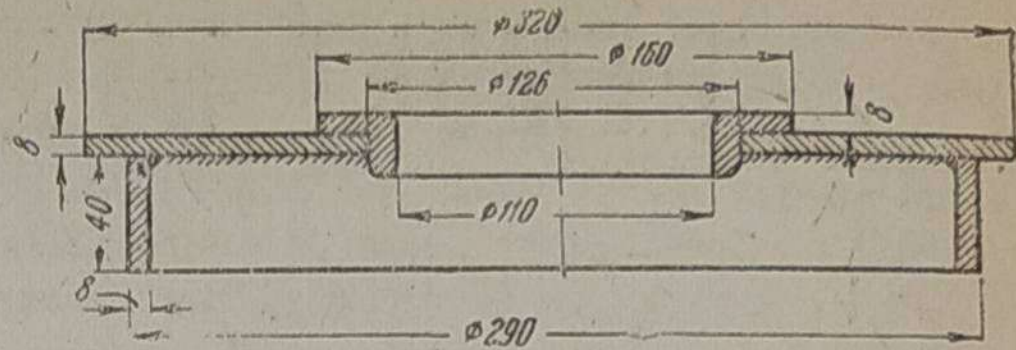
Диск топливника «ХТЗ-Т2Г» в сборе. ка толщиной 2 мм и высотой 40 миллиметров. Внутри корпуса приваривается опорное кольцо, изготовленное из круглого железа диаметром 16 миллиметров. Нижний корпус топливника с указанными деталями в сборе приваривают к воздушному поясу.
